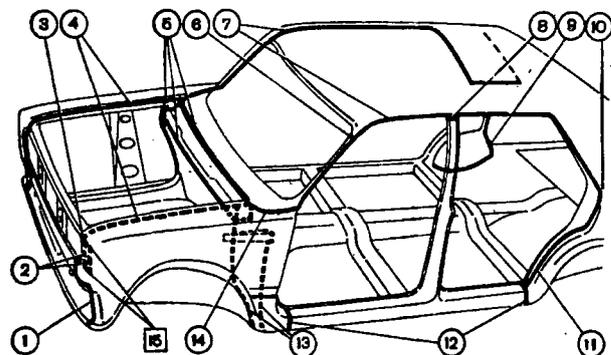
Сварные швы и стыки, на которые наносится уплотнительная мастика (вид кузова слева): 1 - переднего крыла с передней панелью передка; 2 - соединителя крыла с крылом и брызговиком; 3 - усилителя крыла с верхней поперечиной передка; 4 - сточных желобков капота с крыльями и рамой ветрового окна; 5 - щитка передка и коробки воздухопритока с панелью передка и с боковыми панелями; 6 - крыши с рамой ветрового окна; 7 - желобков крыши с панелью и боковинами крыши; 8 - верхнего торца центральной стойки; 9 - пола с основаниями чашки пружины задней подвески и арками задних колес; 10 - наружных угловых панелей с задним крылом; 11 - заднего крыла с боковиной; 12 - порогов пола с крыльями; 13 - боковины с внутренними панелями передка; 14 - крыла с рамой ветрового окна; 15 - угол соединителя крыла с крылом и брызговиком
